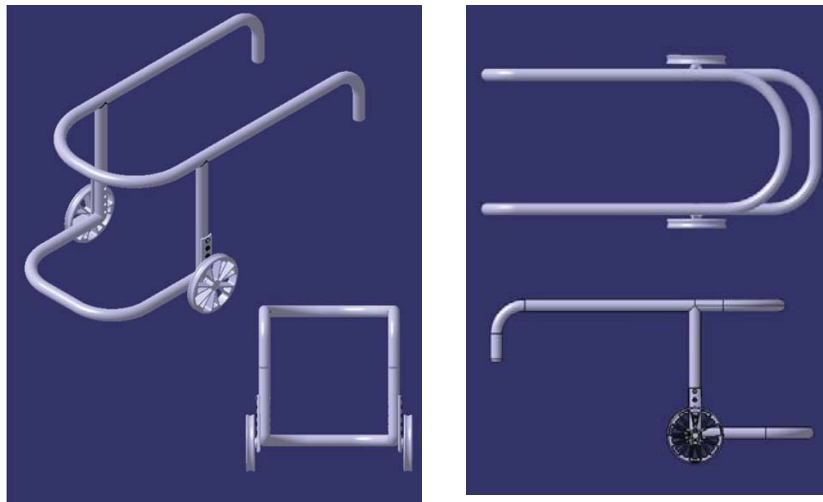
Cărucior cu role (vedere izometrică și frontală)
